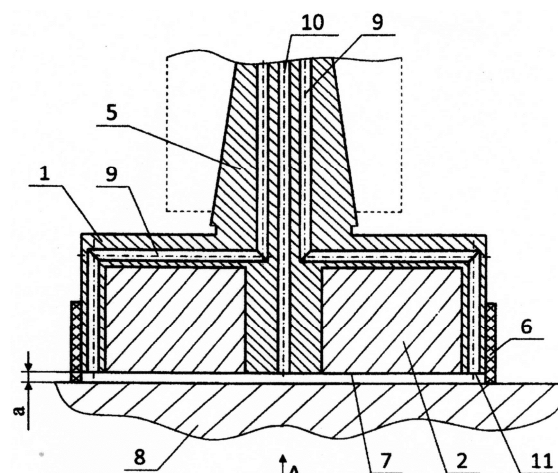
Устройство для магнитно-абразивной обработки патент RU №2220836
